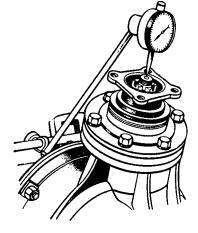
Проверка осевого зазора в подшипниках вала ведущей шестерни главной передачи
